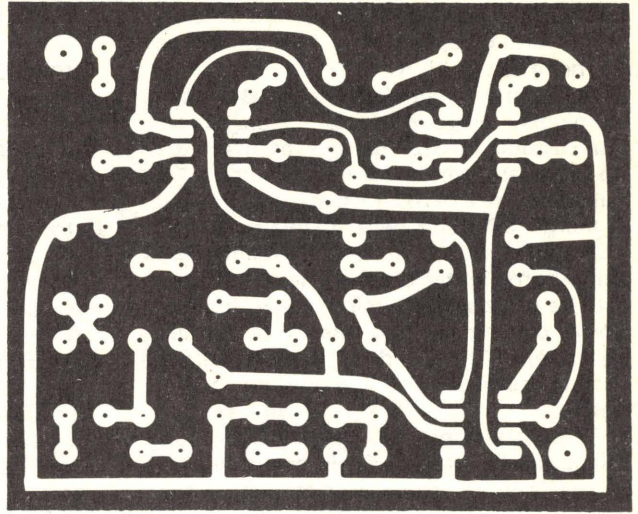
Disegno del circuito stampato e disposizione dei componenti.
